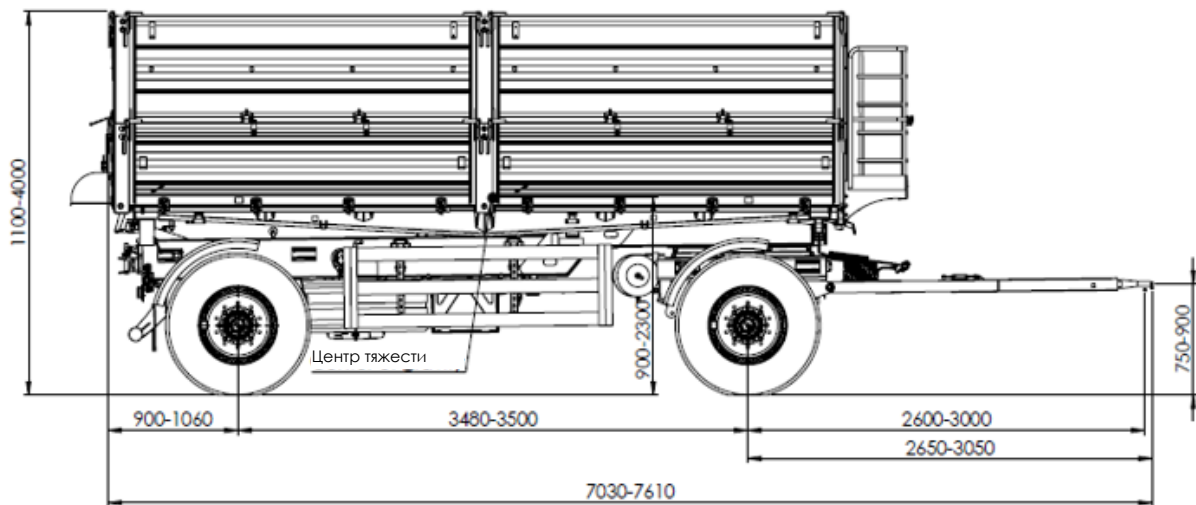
Размеры прицепа Т958 - вид сбоку
